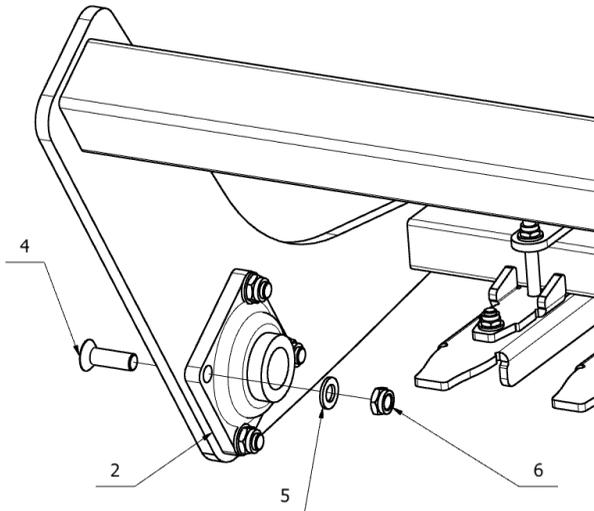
U-Profil-Walze Ø520mm – Lagermontage.
